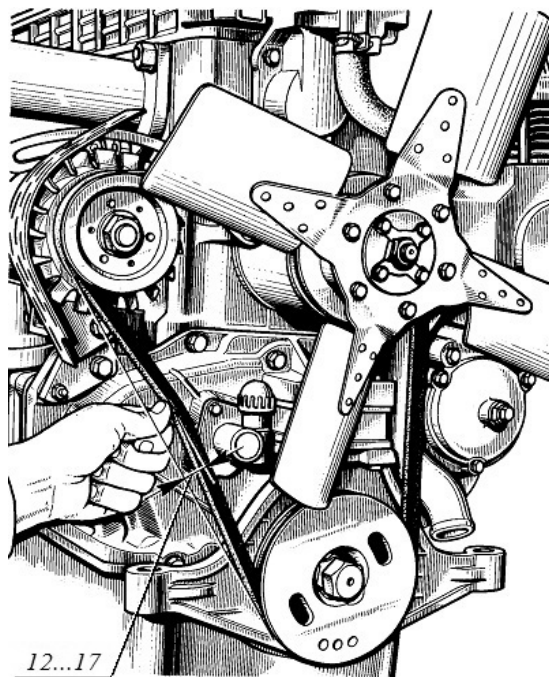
Регулировка натяжения ремня вентилятора двигателя Д-245
